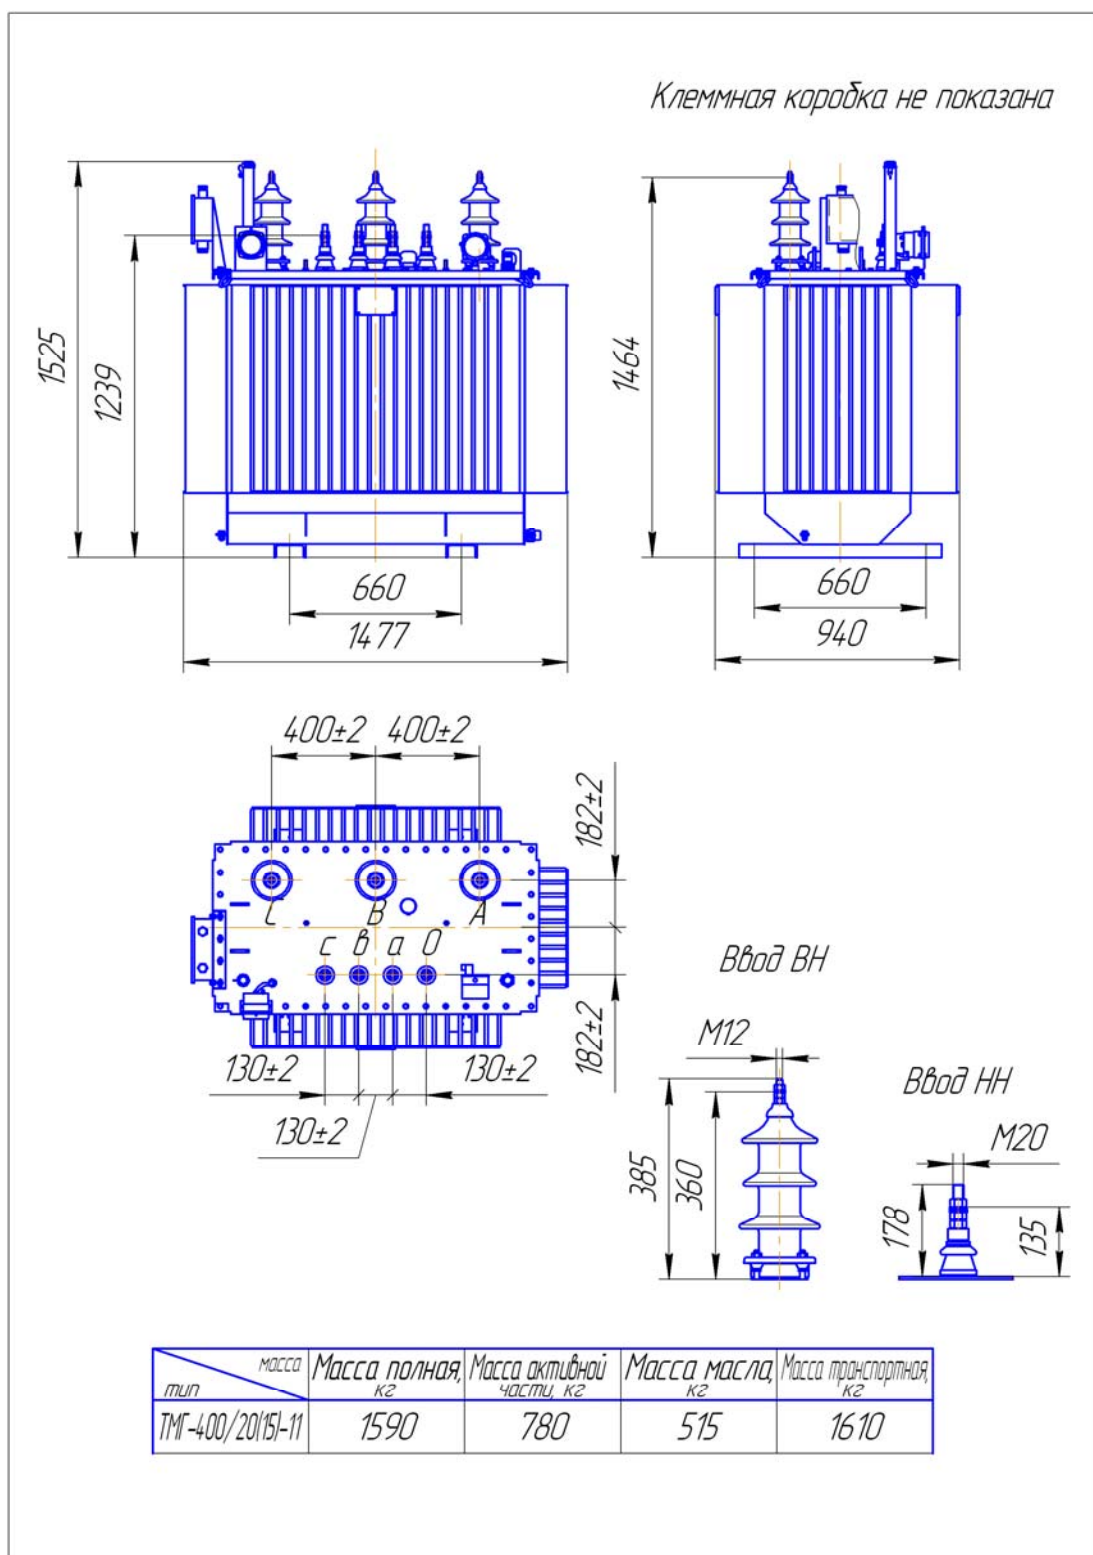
Габаритные, установочные и присоединительные размеры трансформатора ТМГ - 400/20-11
